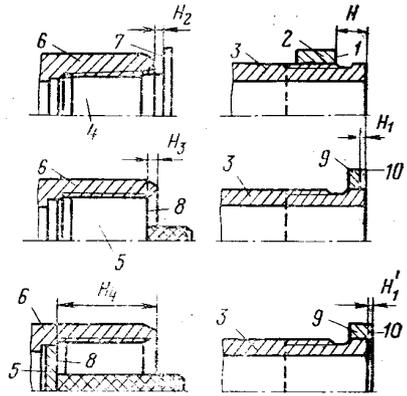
Контроль калибрами резьбовых соединений насосно-компрессорных труб НКМ:
